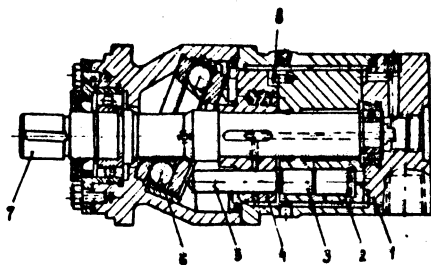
Рис. I. Конструкция аксиально-поршневого гидромотора: 1—опорный диск; 2—ротор; 3—пistonь; 4—барaban; 5—толкатель; 6—шарикоподшипник; 7—вал
